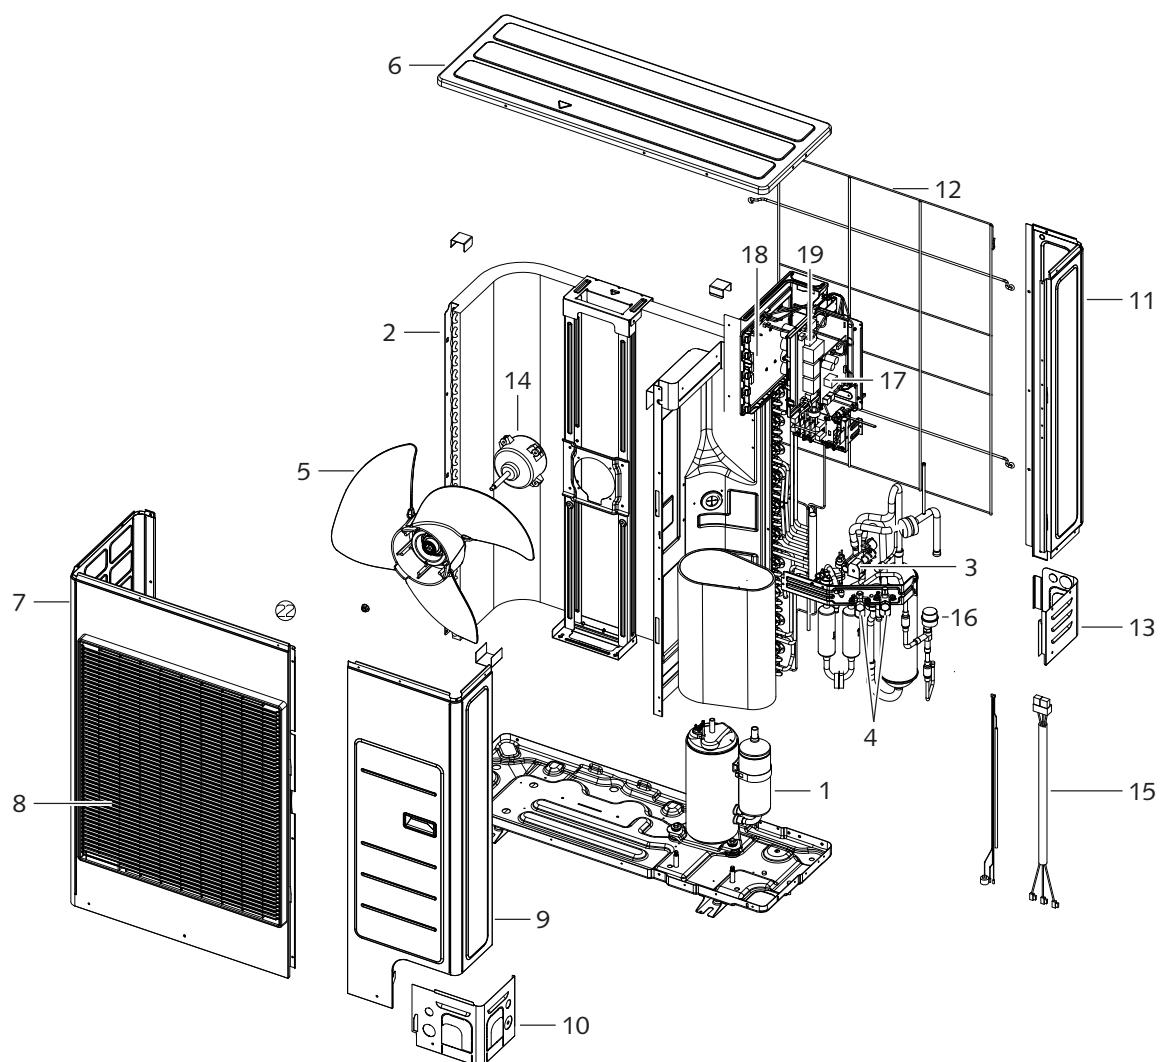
Explosionszeichnung Außenmodul WKF 120 Duo
